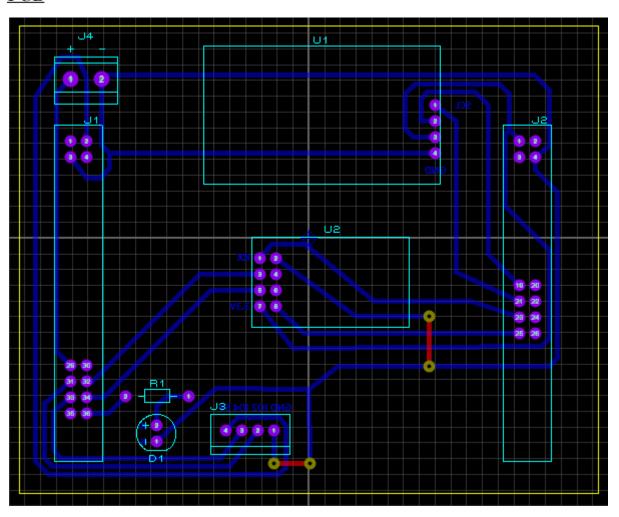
Diagrama del PCB completo en la vista "PCB Layout"
